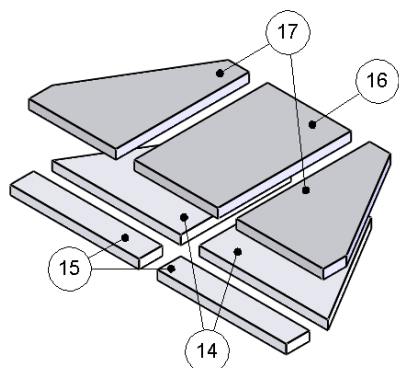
Installation des panneaux isolant du fond pour les pierres réfractaires en ciment
